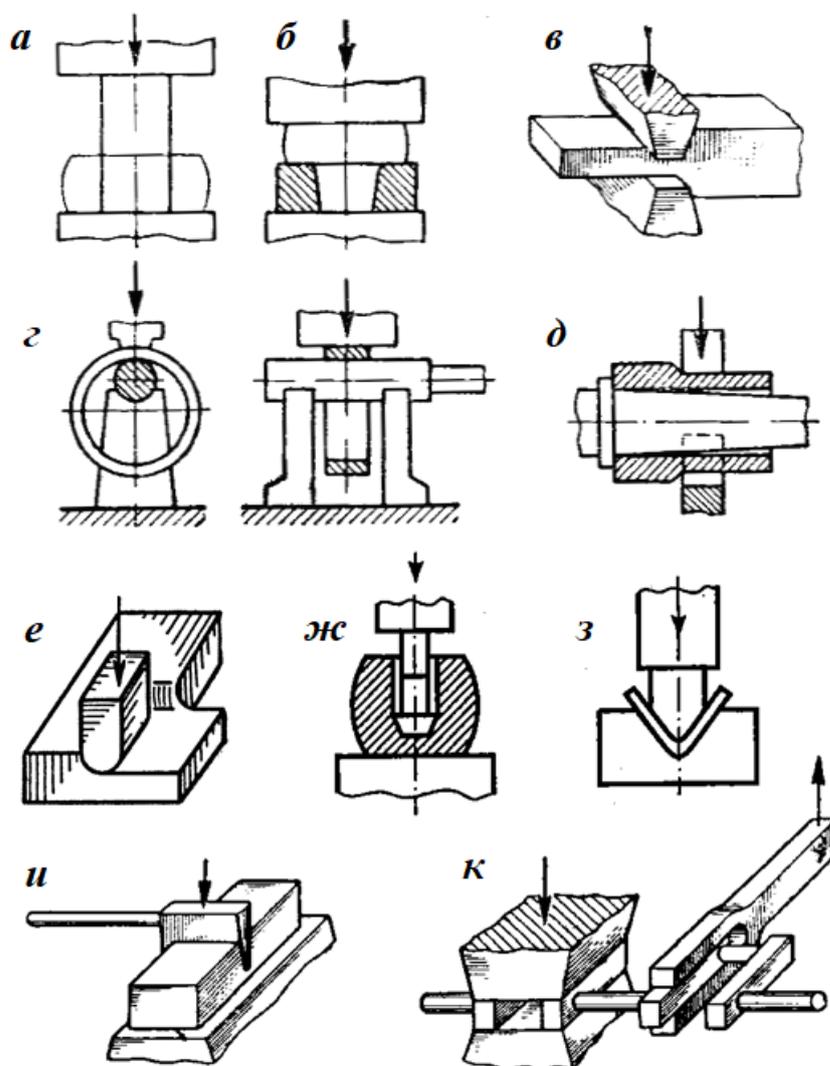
Основные операцииковки: а – осадка; б – высадка; в – вытяжка плоскими бойками; г – раскатка на оправке; д – вытяжка на оправке; е – разгонка; жс – прошивка; з – гибка; и – рубка; к – скручивание
